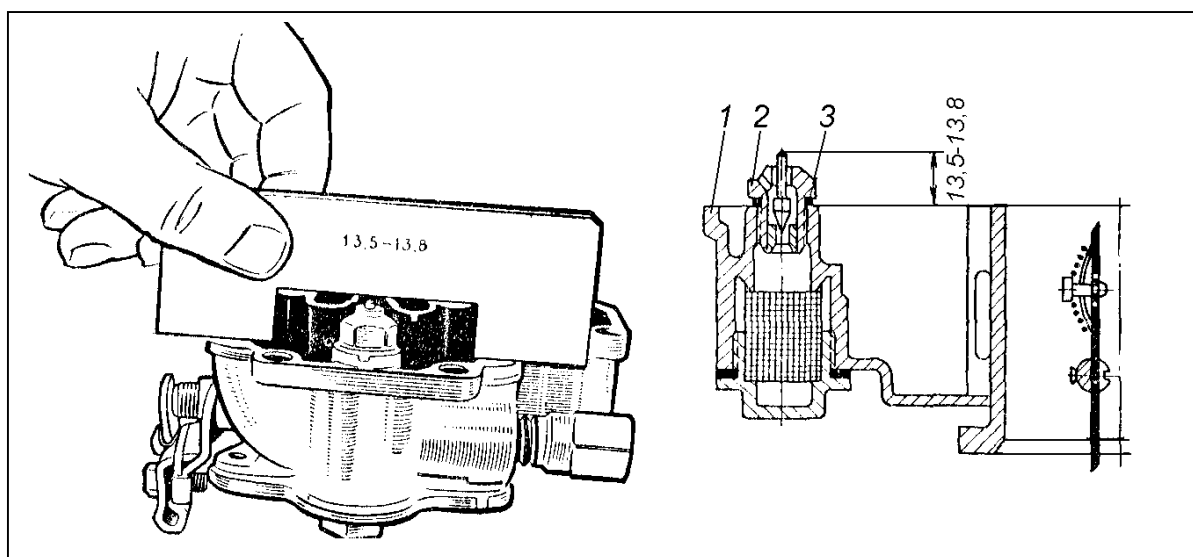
Проверка установки клапана поплавковой камеры карбюраторов К-88А и модиф.:
